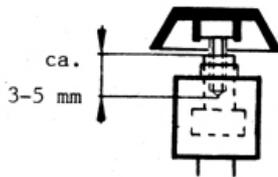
Ausgebaute Taste BO mit eingeschraubter Kappe
